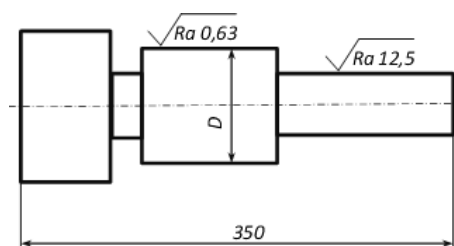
Вал ступенчатый (материал - группа стали  $M1$  или  $M2$ ; заготовка - штамповка на ГКМ)
